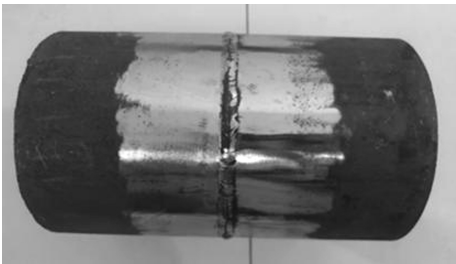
常减压装置管道焊接接头打磨抛光实物图
